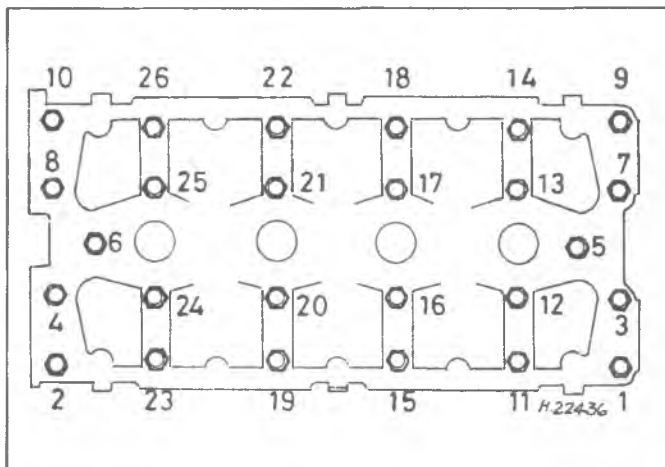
Последовательность затяжки болтов корпуса подшипников распределительных валов
